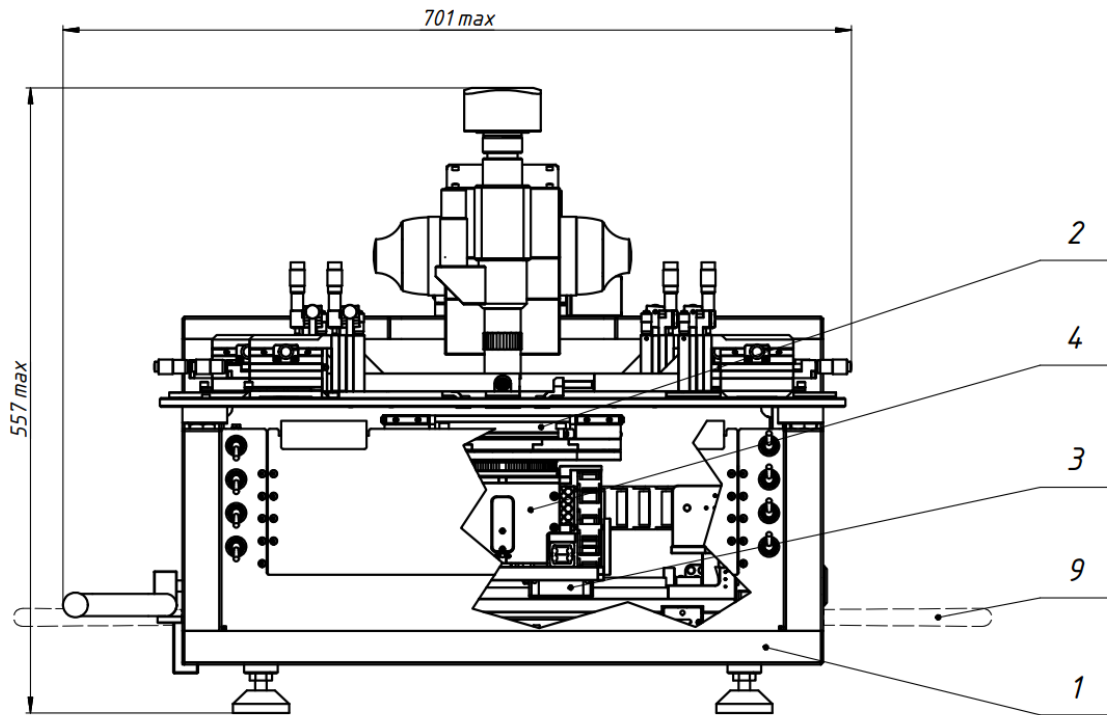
Габаритный чертёж полуавтоматической зондовой станции Terra-200COAX вид
